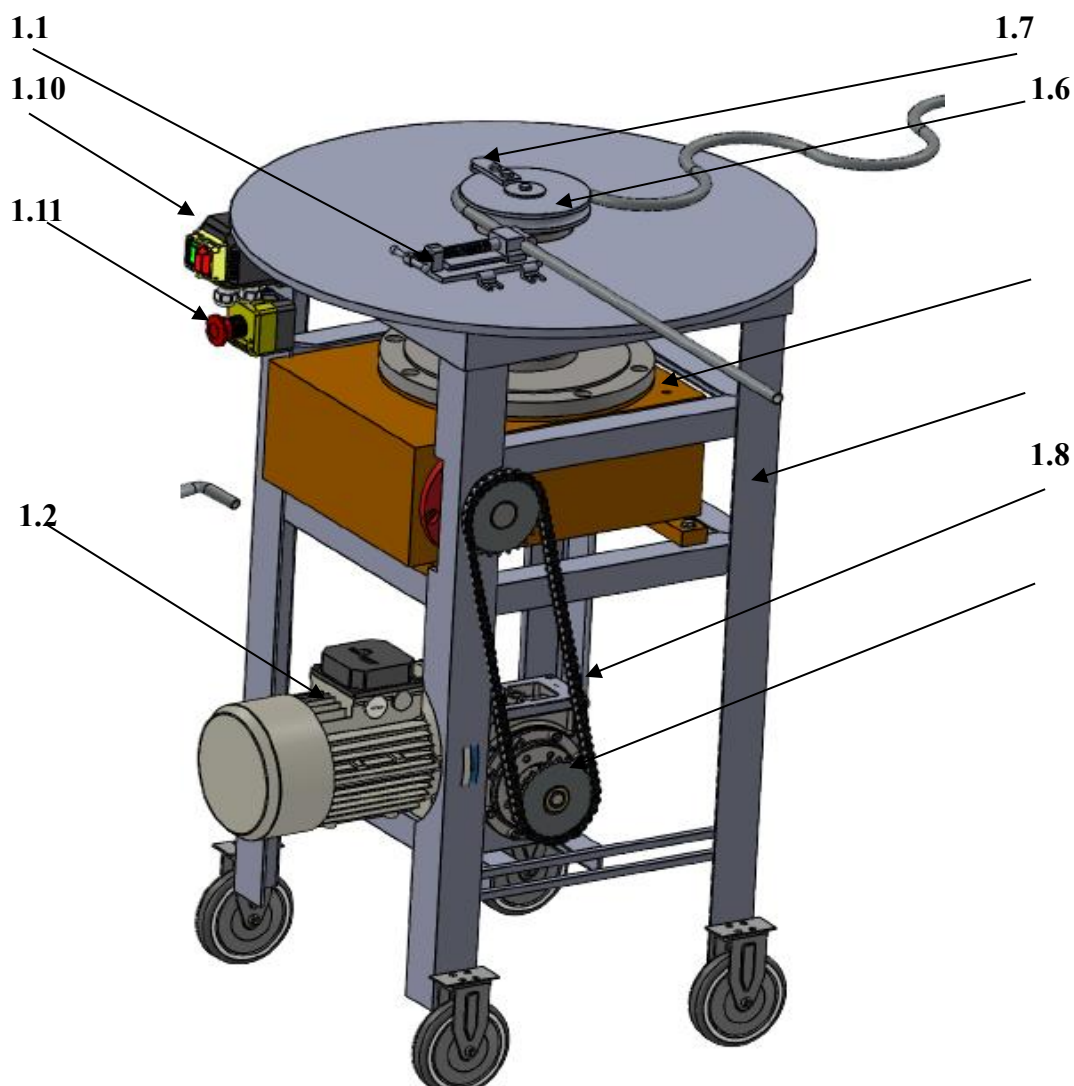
(a): Vue dessous - vue isométrique de l'assemblage de la cintruse plane
